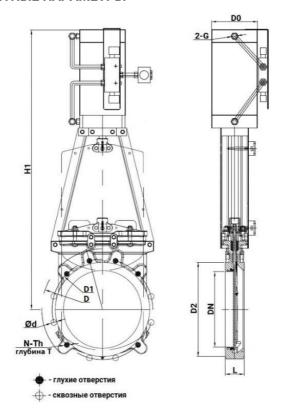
Размеры задвижки в сборе с пневмоцилиндром
